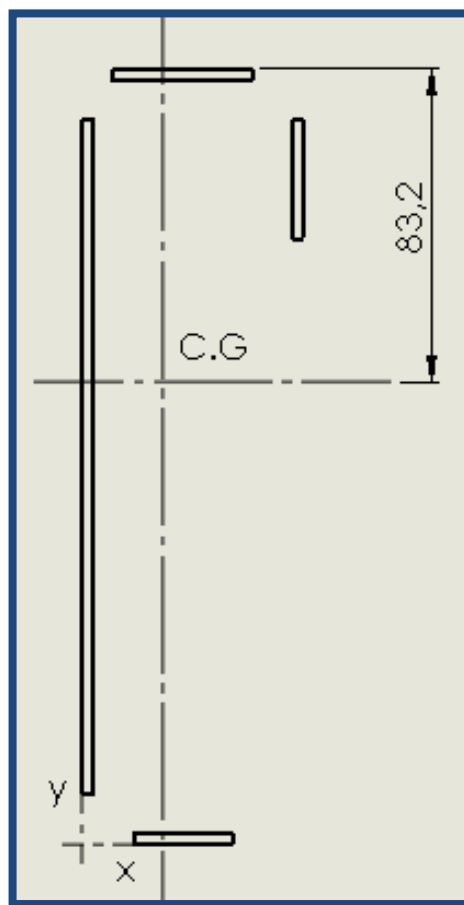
Disposición de los cordones de soldaduras y referencias.
